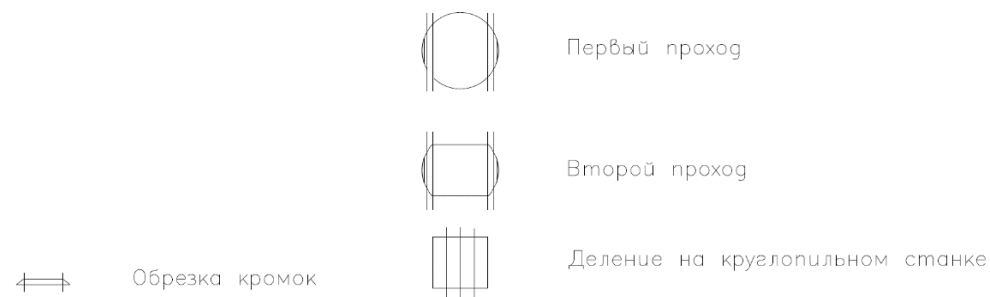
Схема раскроя бревен на ленточнопильной лесопильной линии
